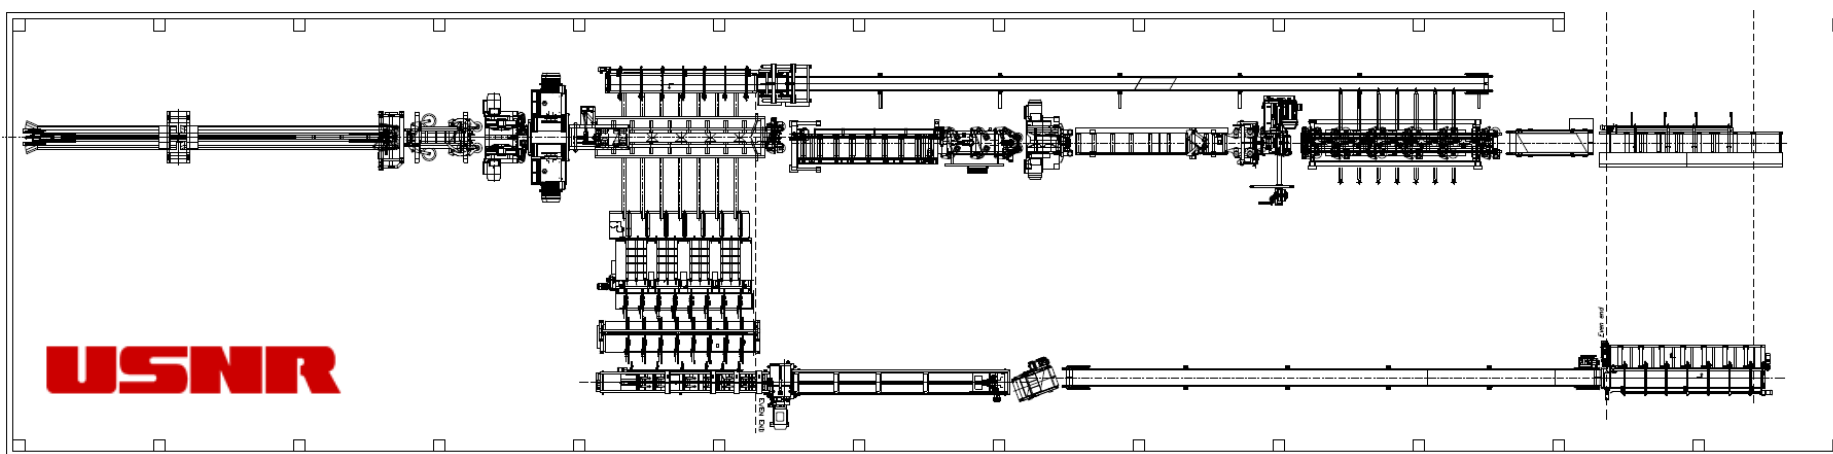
Лесопильная линия на базе круглопильного оборудования [10]
